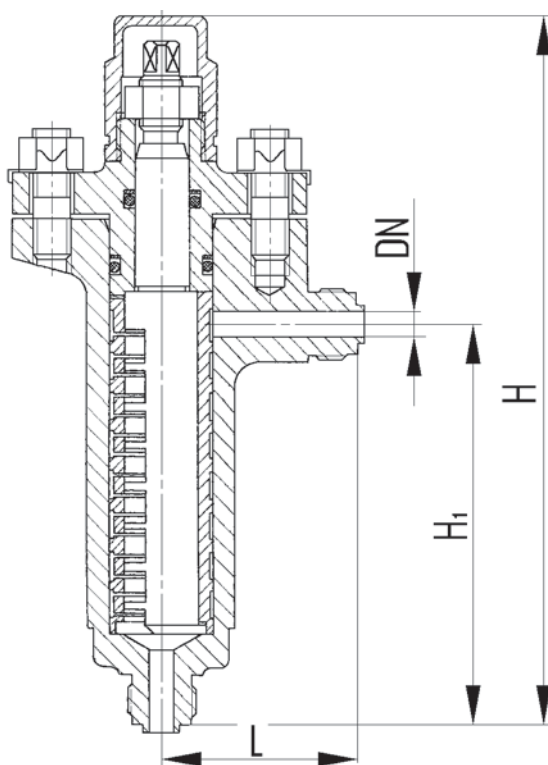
Клапан дроссельный угловой штуцерный
